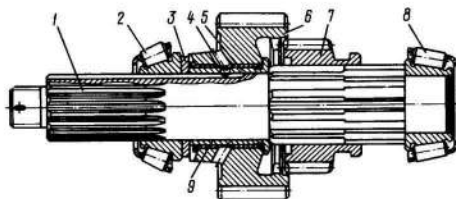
Первичный вал в сборе: 1 — шлицевый конец вала; 2, 8 — подшипники; 3 — упорная шайба; 4 — штифт; 5 — стальная втулка; 6 — ведущая шестерня; 7 — шестерня включения второй и первой передач; 9 — бронзовая втулка
